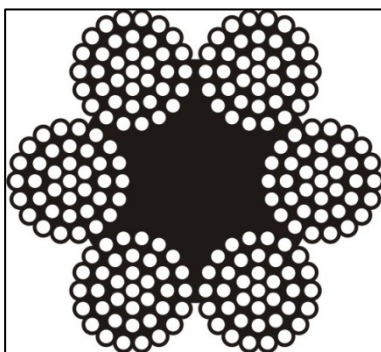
Konstrukce SEAL s textilní vložkou [10]
